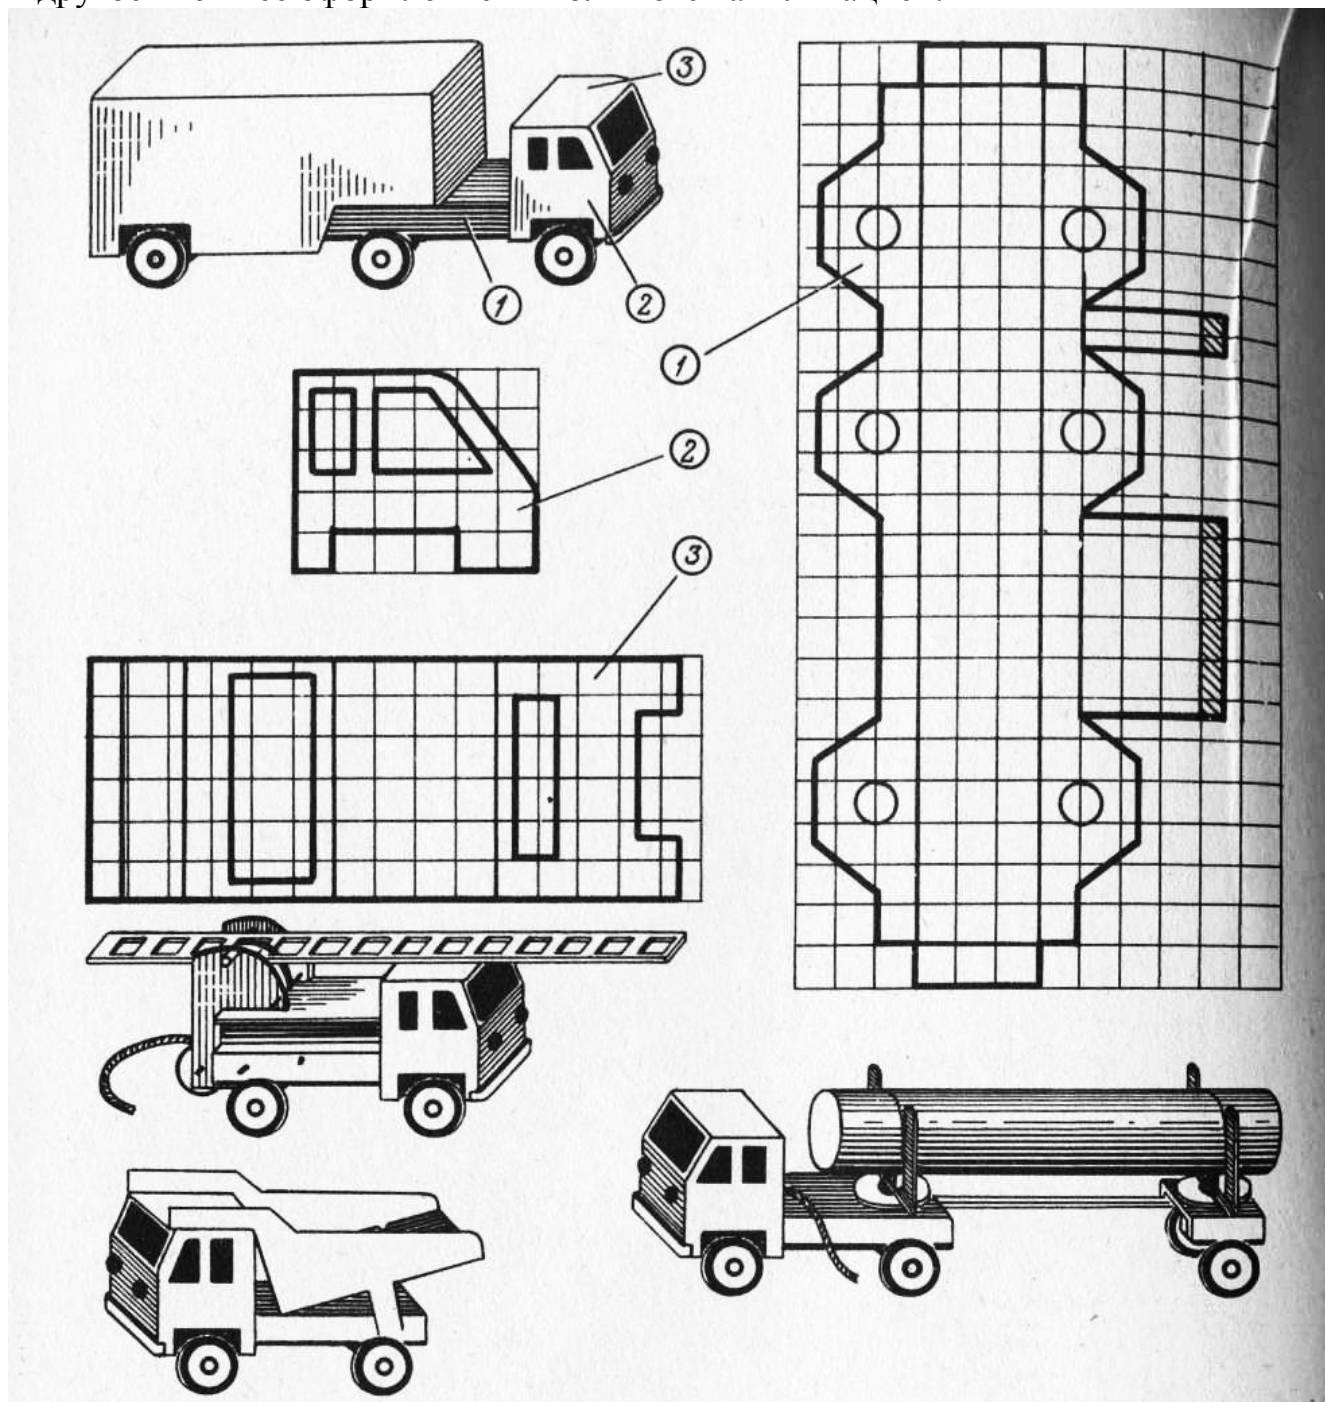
Модель грузовика КамАЗ: 1— рама; 2— боковая стенка кабины; 3— развертка задней и передней стенки кабины вместе с крышей; наглядные изображения грузовиков с различными видами кузовов
